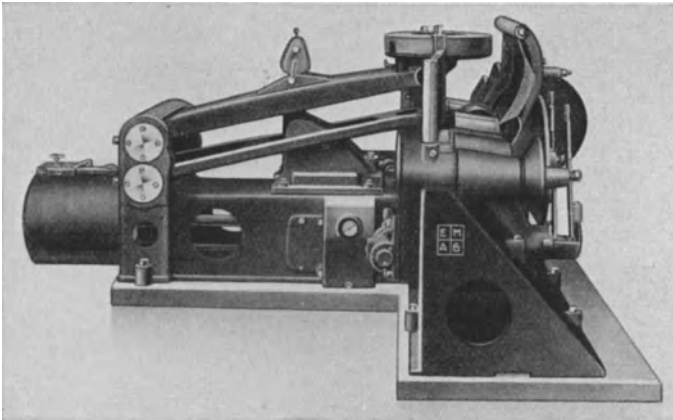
Vorschälmaschine der Eisengießerei und Maschinenfabrik A. G. Bautzen.
